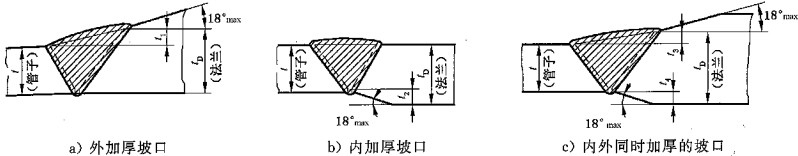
无衬环的对焊法兰的焊接坡口型式及尺寸
